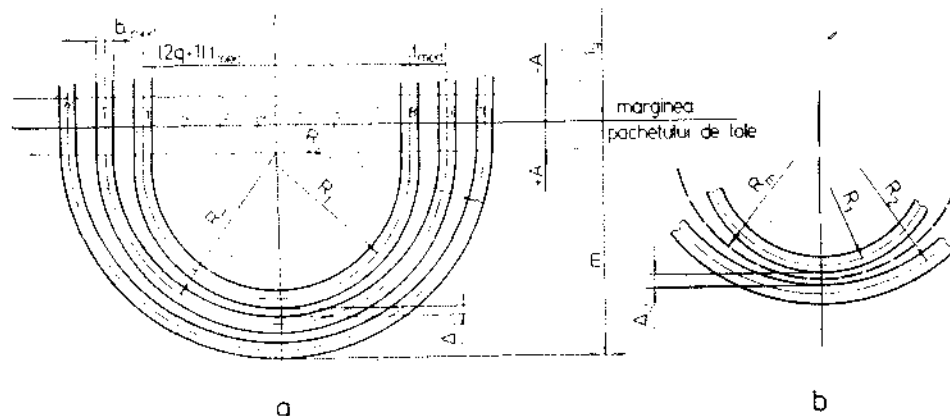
Dimensionarea capătului de bobină pentru înfășurarea într-un strat, cu capetele grupelor de bobine de aceeași formă și $q = 3$.
